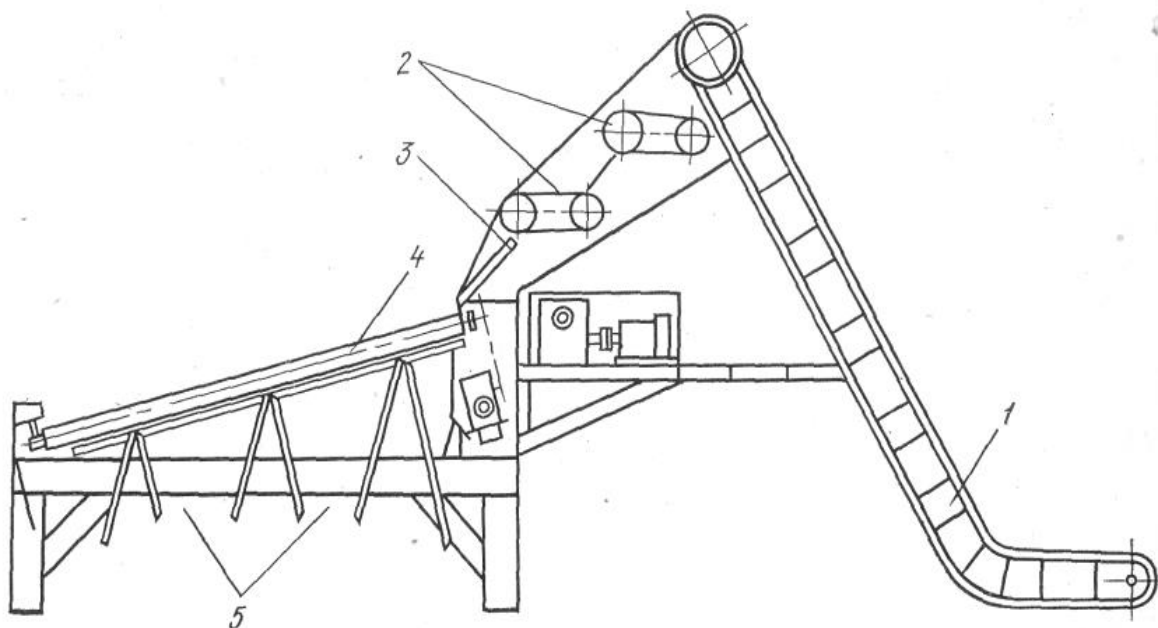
Агрегат ИСП для сортирования рыбы:
